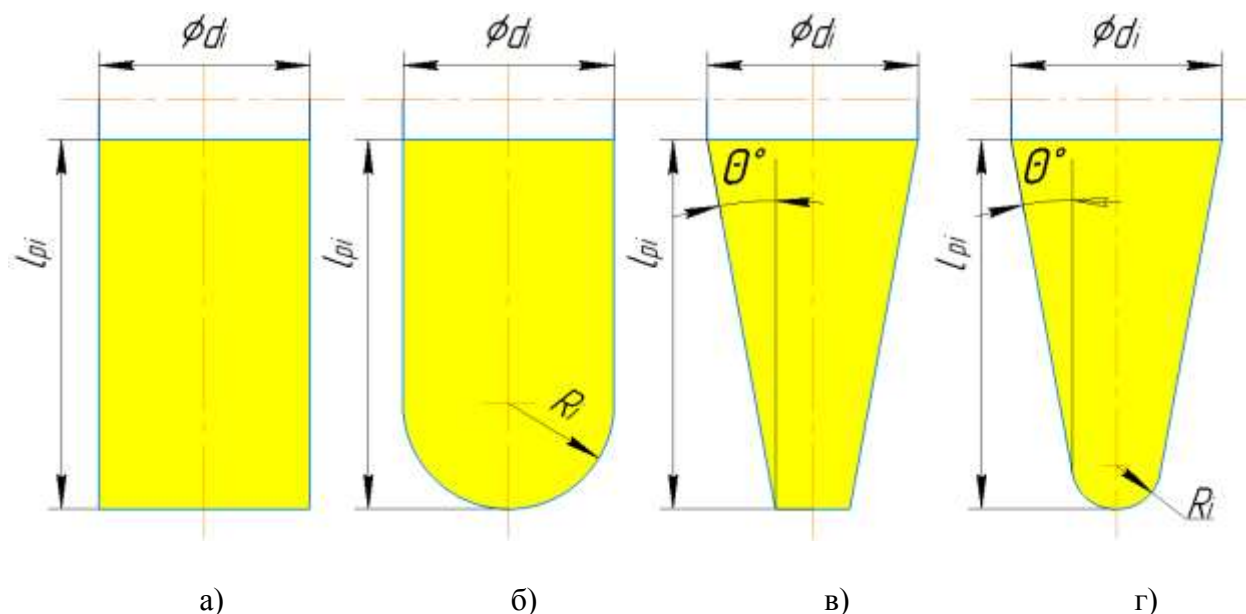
Різальні інструменти для обробки складних поверхонь деталей на трьохкоординатних фрезерних верстатах з ЧПК: циліндрична (а), сферо-циліндрична (б), конічна (в), сферо-конічна (г).
